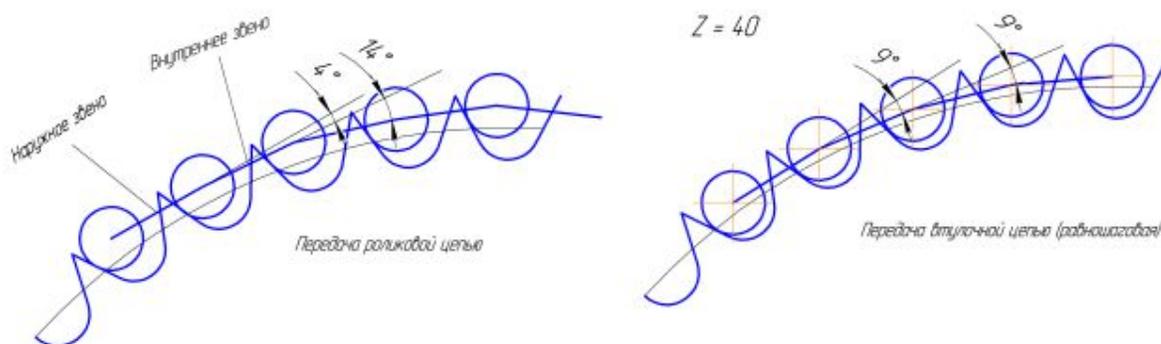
Расположение шарниров роликовой и втулочной цепей на звёздочке в 40 зубьев
